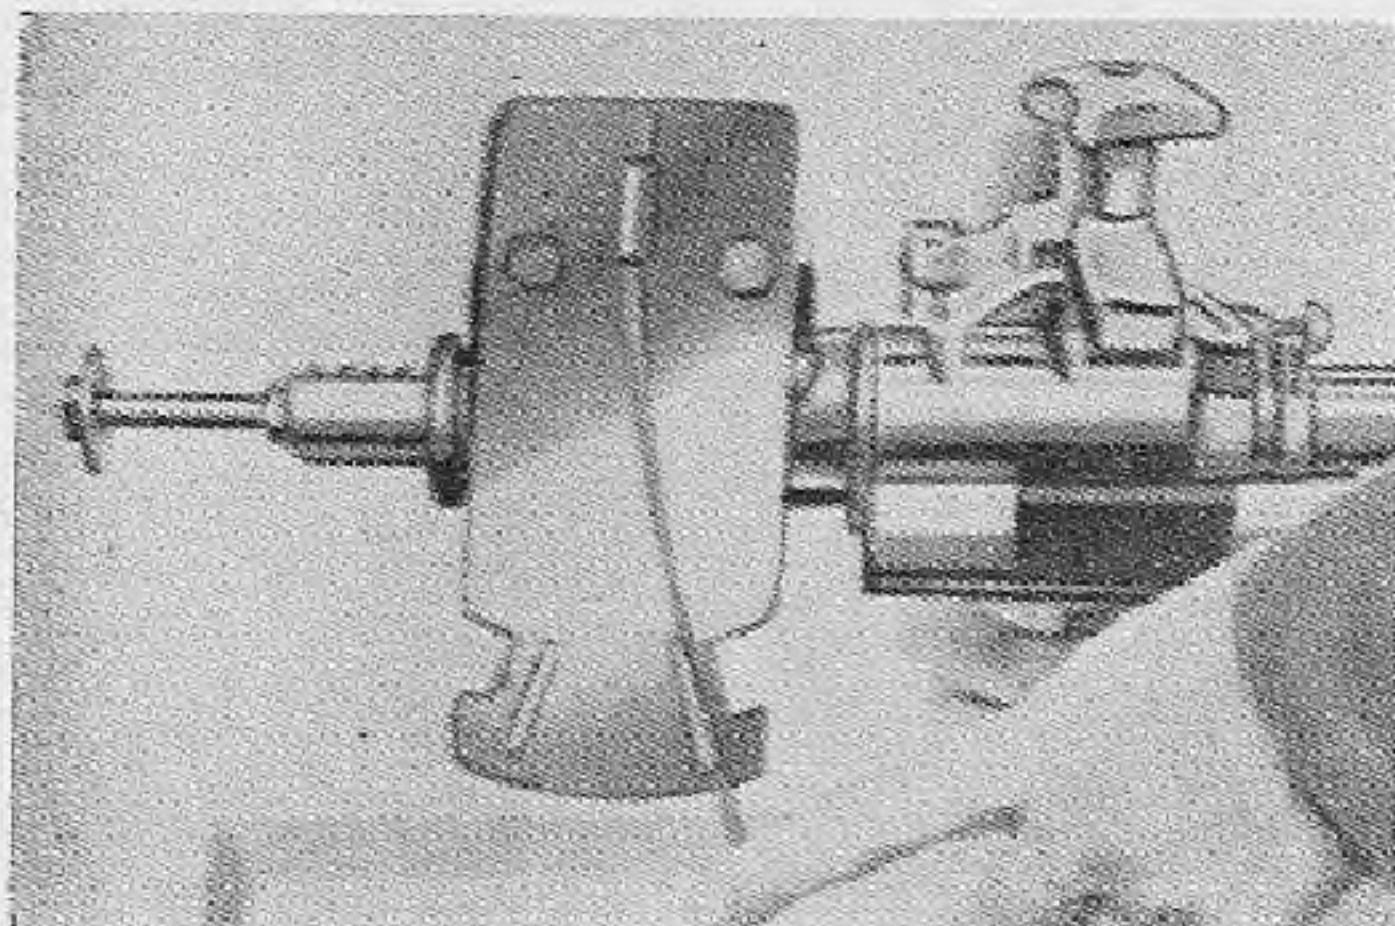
Posición de la varilla del dispositivo DK 114 para la regulación del par motor.
